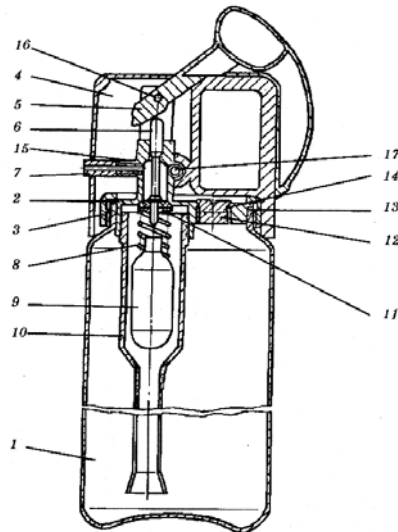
Будова вогнегасника ОП-1В «Момент-2»: 1 – корпус; 2 – головка; 3 – гайка накидна; 4 – ковпак; 5 – важіль запуску й керування клапаном; 6 – голка; 7 – насадок-розпилювач; 8 – пружина; 9 – балон з робочим газом; 10 – лгрубка сифонна; 11 – клапан; 12 – пробка; 13 – кільце ущільнювальне; 14 – кільце ущільнювальне; 15 – кільце ущільнювальне; 16 – вісь; 17 – гвинт
